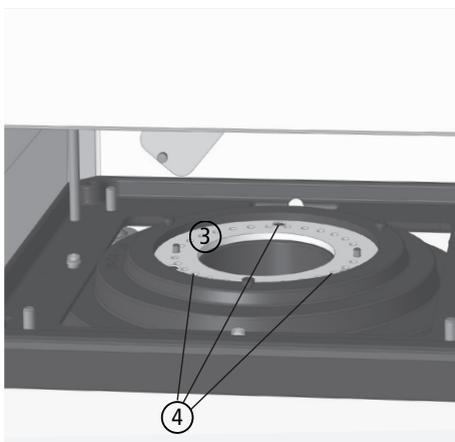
Démontez la rondelle de réglage des butées latérales
